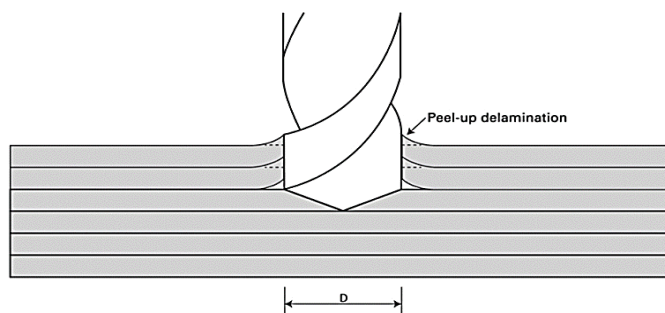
Схема деформацій розшарування на вході інструменту [2]
